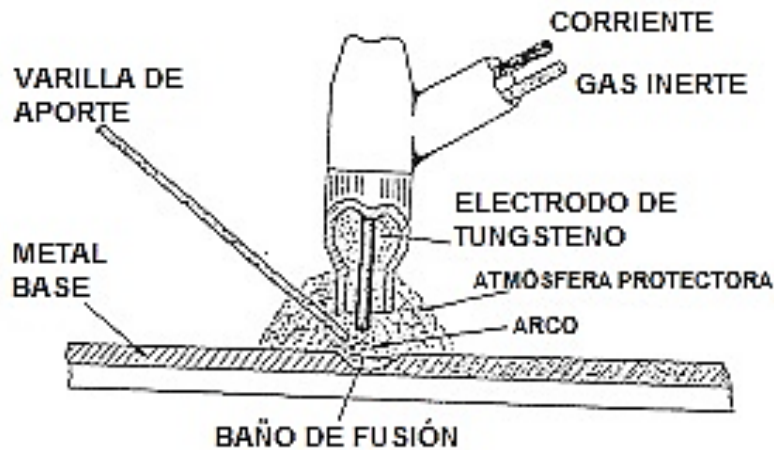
Soldadura tipo TIG (Ingemecánica, s.f.)
